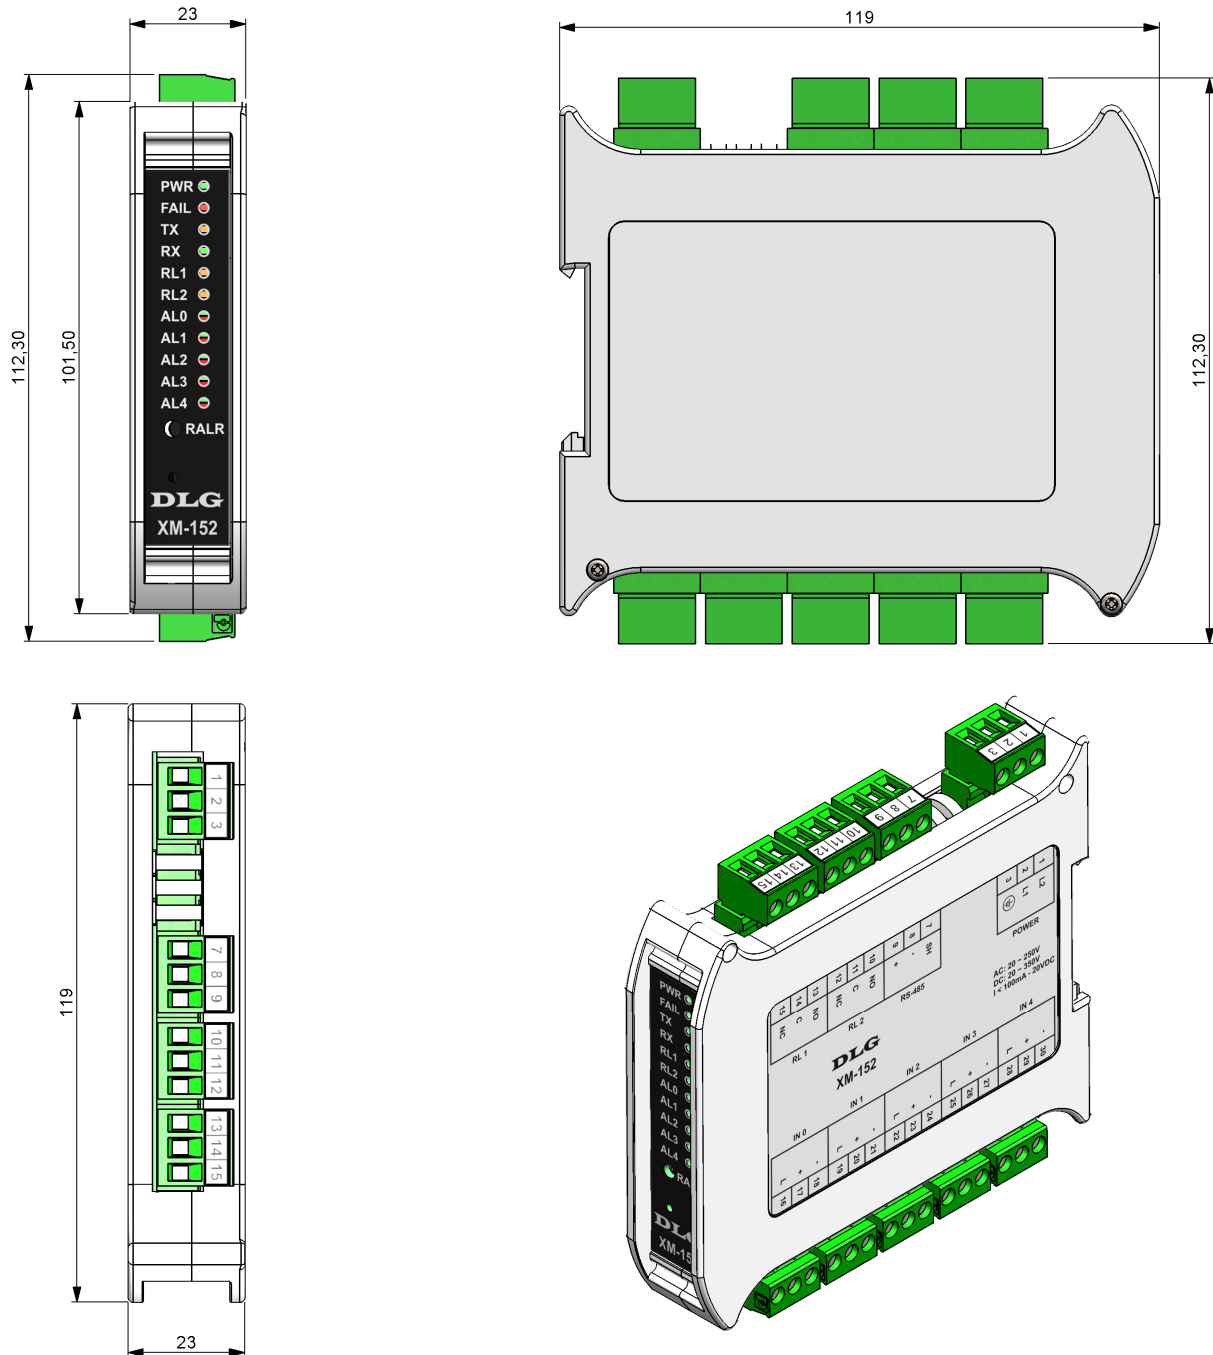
Dimensionamento para montagem (Cotas em milímetros)
